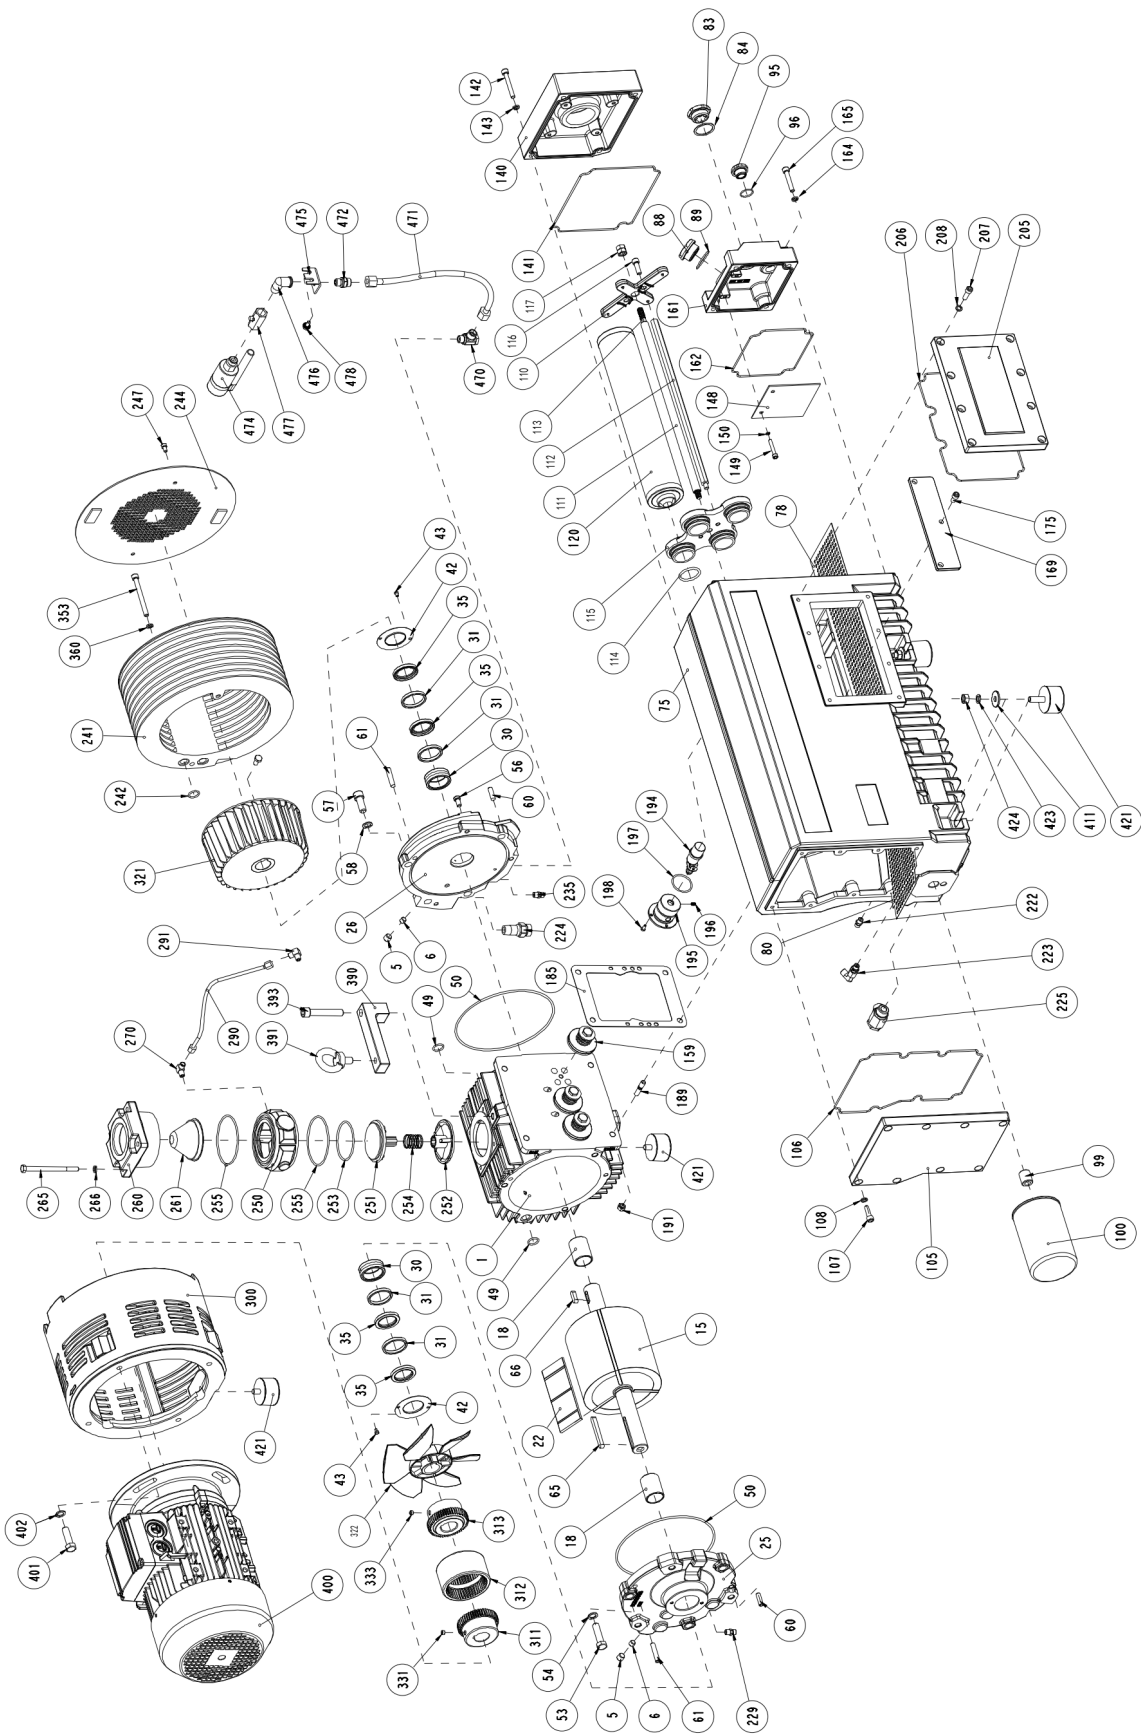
Explosionszeichnung der Modelle -0250 / -0300
